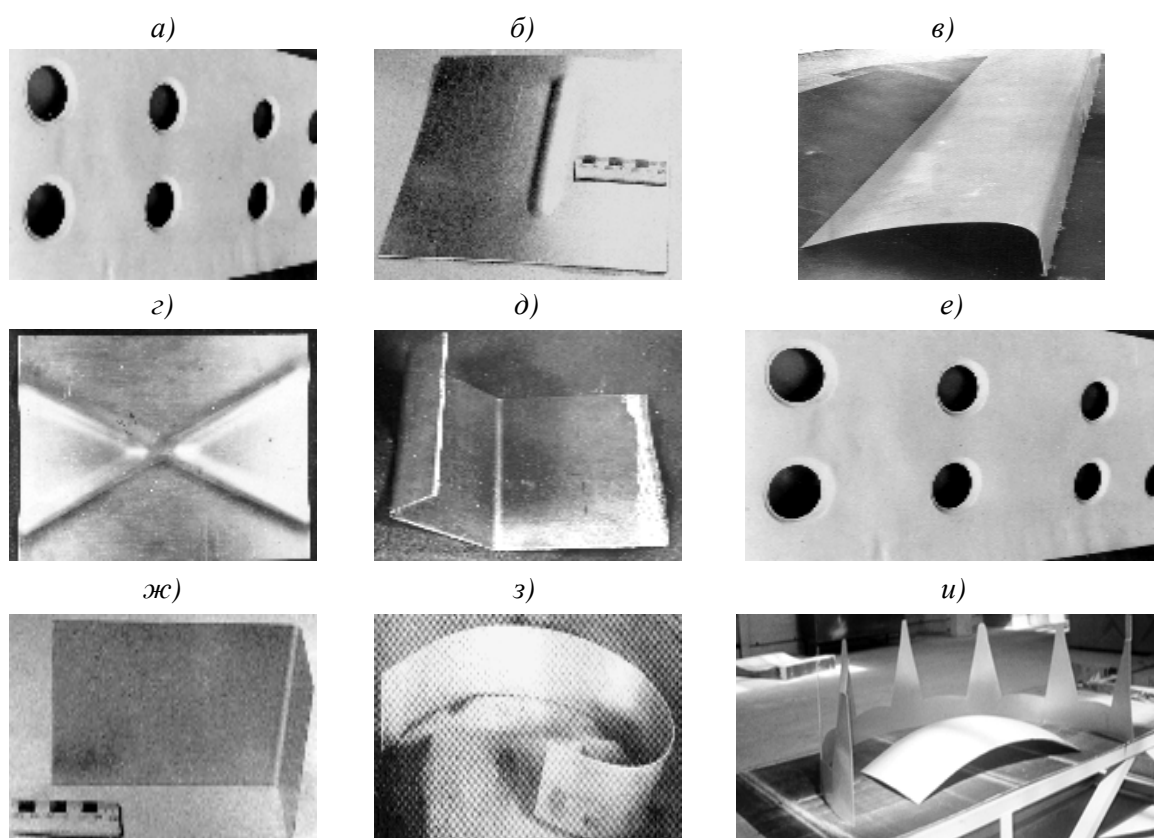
Образцы деталей, полученных пластическим деформированием из листов МПКМ: а – отбортовка (штамповка эластичной средой); б – рифт (штамповка эластичной средой); в – обшивка носка крыла; г – перекрещивающиеся рифты (штамповка эластичной средой); д – образец гнутый (углы изгиба 60–70 град); е – фрагмент стенки балки с отбортовками тарельчатой формы; ж – образец гнутый (угол изгиба 90 град); з – образец (гибка–прокатка на радиусы 500–100 мм); и – образцы обшивок реверса РУ-18Т (корона) и мотогондолы двигателя Д18Т (изготовлены обтяжкой)
